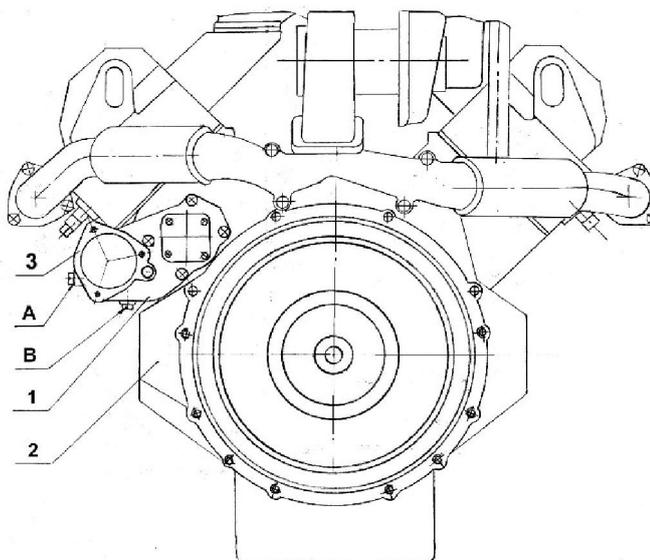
Установка редуктора привода насоса забортной воды на двигателе:
